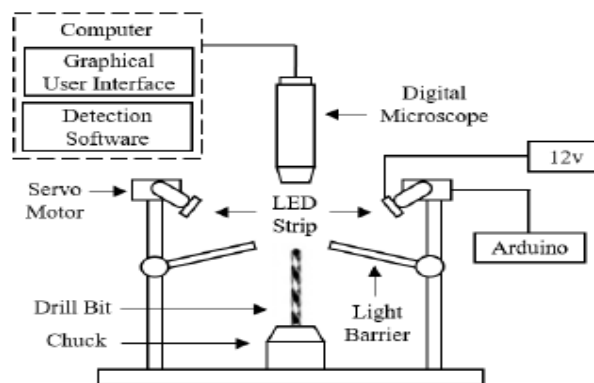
Método de inspeção de ferramentas de escarear e furar
